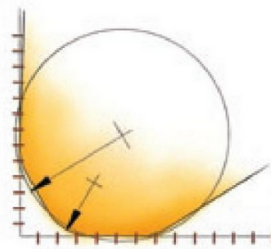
Схема вершини різальної частини інструменту, виготовленого за технологією Wiper
